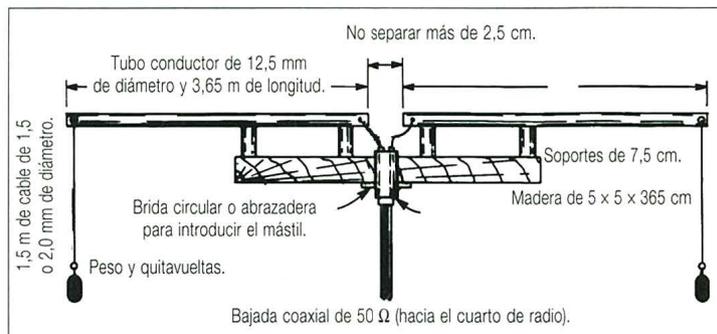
Esquema del dipolo giratorio para 20 metros. Los detalles constructivos se exponen en el artículo.
